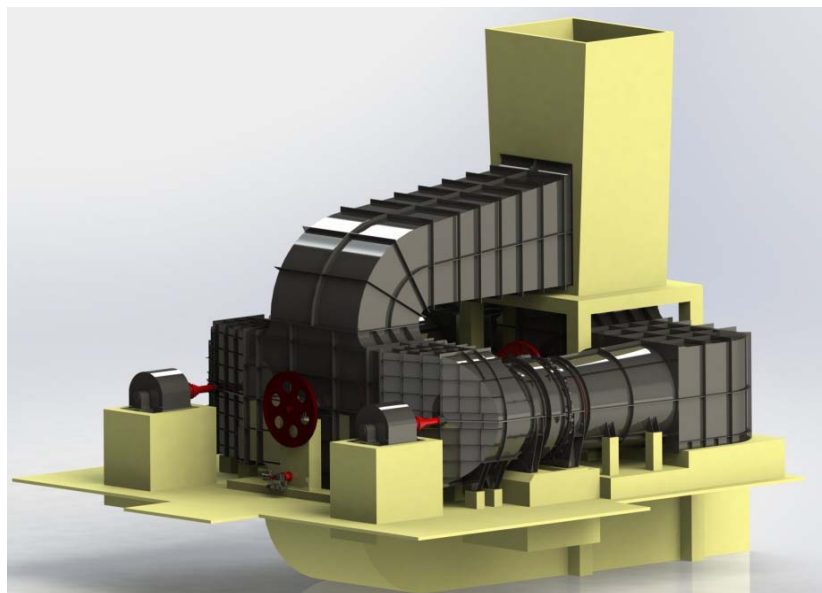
Компактная вентиляторная установка без здания и укрытия
